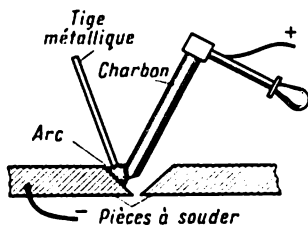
Soudage électrique par la méthode de Benardos (à électrode de charbon)
